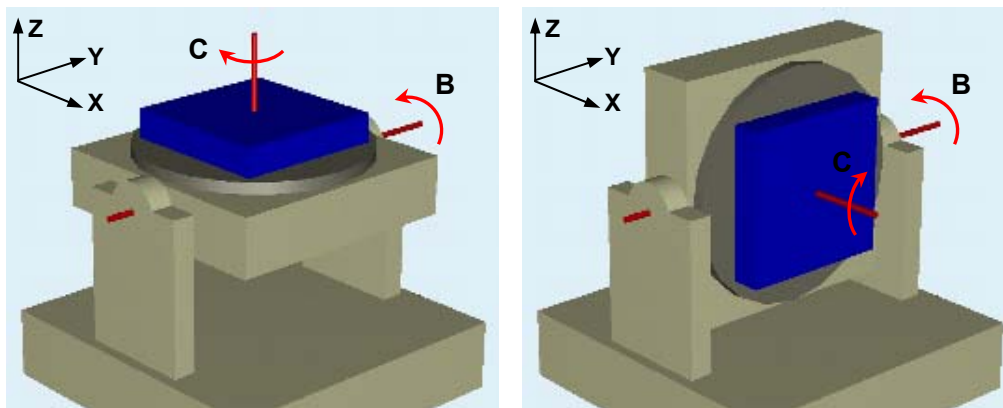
(c) Координаты положения рабочих органов станка $B0C0$ Рис. 22.9 (d) Координаты положения рабочих органов станка $B-90C0$
